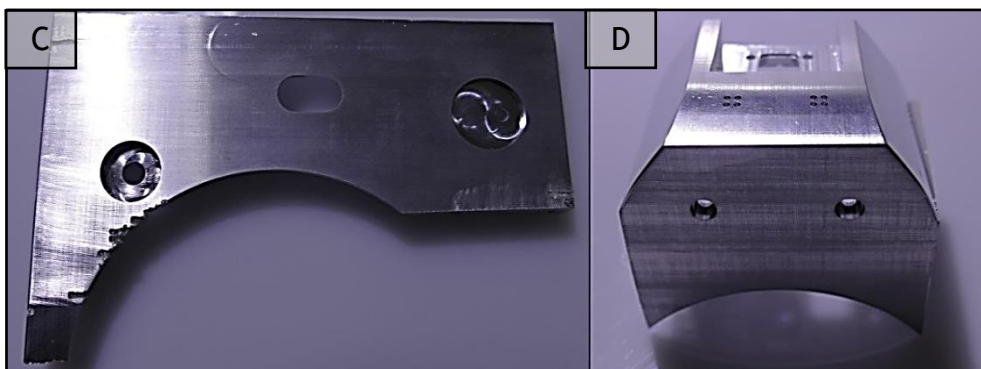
Exemplo do corte de um dos componentes utilizando a serra de corte manual.
